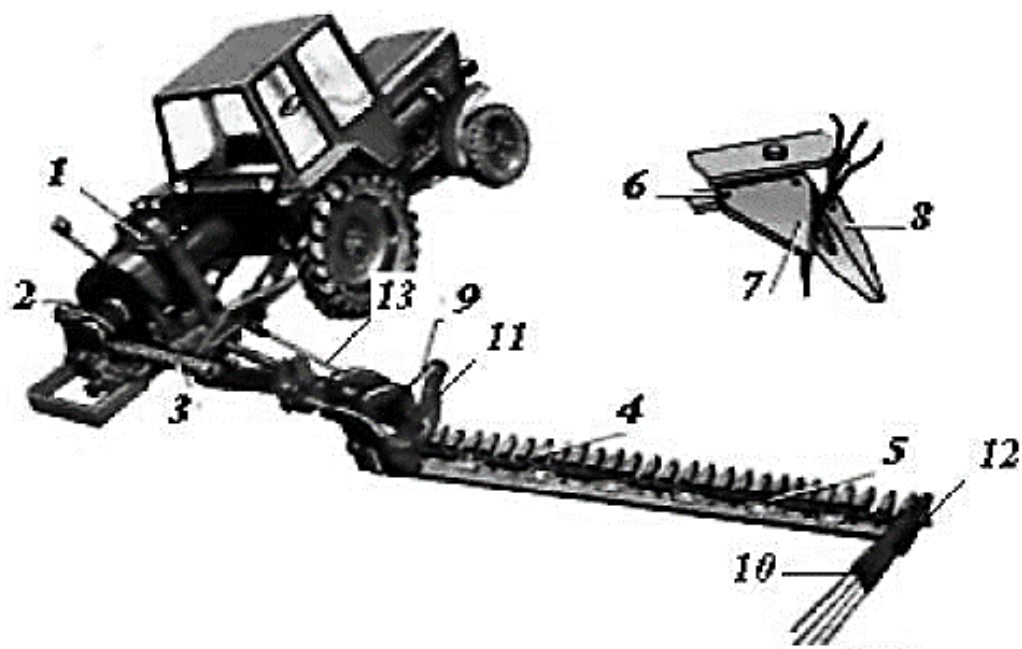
Косилка КС-Ф-2,1: 1 – навеска; 2 – механизм привода; 3 – механизм уравнивания; 4 – брус пальцевый; 5 – нож; 6 – спинка ножа; 7 – сегмент; 8 – палец; 9 – делитель; 10 – полевая доска; 11 – внутренний башмак; 12 – внешний башмак; 13 – шпренгель
